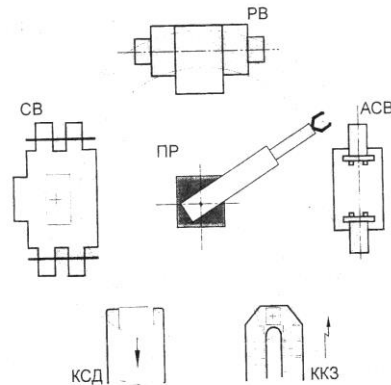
Схема РТК для обробки литих деталей диференціала автомобіля: ККЗ - конвеєр кроковий для заготовок; АСВ - агрегатно-свердлувальний верстат; РВ - розточувальний верстат; СВ - свердлувальний верстат; КСД - конвеєр стрічковий для деталей.
